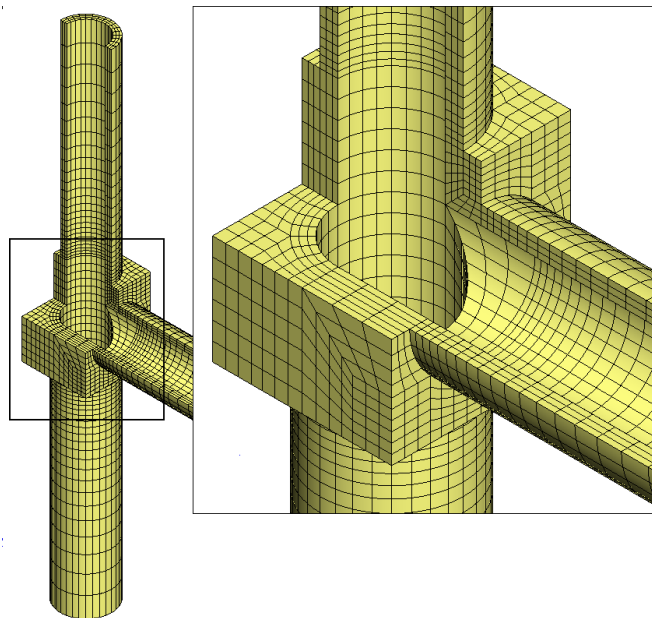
Сварное соединение труб. ИПКЭ20
